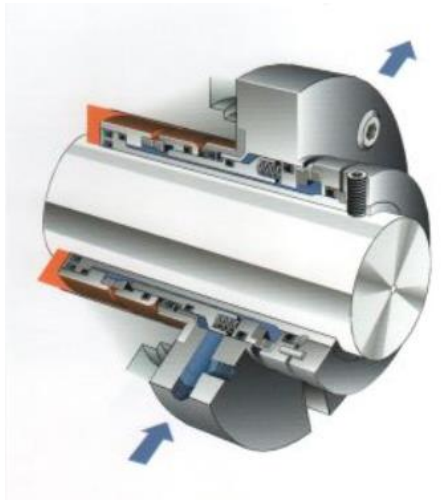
1.15 Sección del cierre mecánico doble SB2 del fabricante John Crane.
